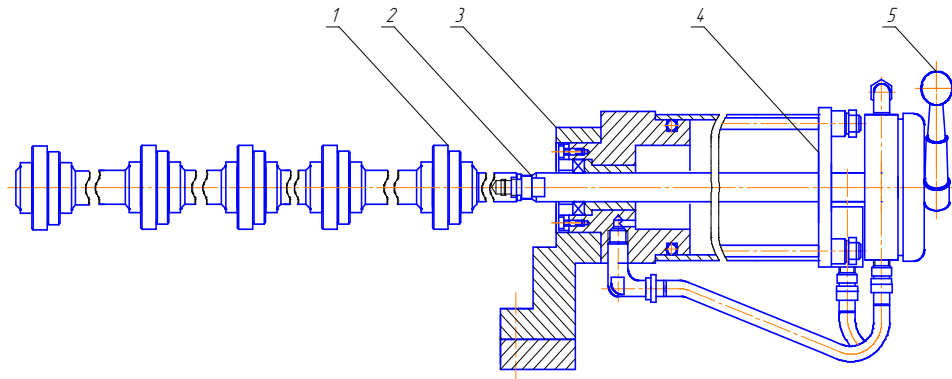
Загальний вид пристосування для заміни втулок розподільчих валів з пневмоприводом: 1—пристрій в зборі; 2—затискач; 3—корпус; 4—пневмоциліндр; 5—рукоятка керування пневмоциліндром
